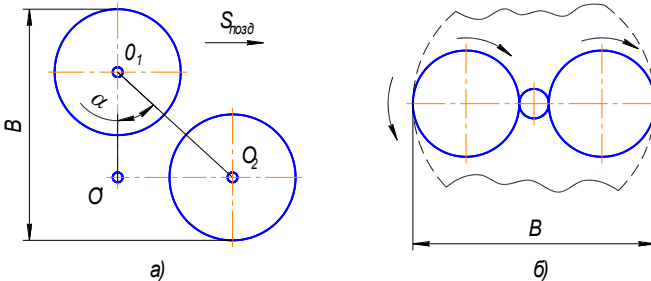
Способи фрезерування неперервної плоскої поверхні
